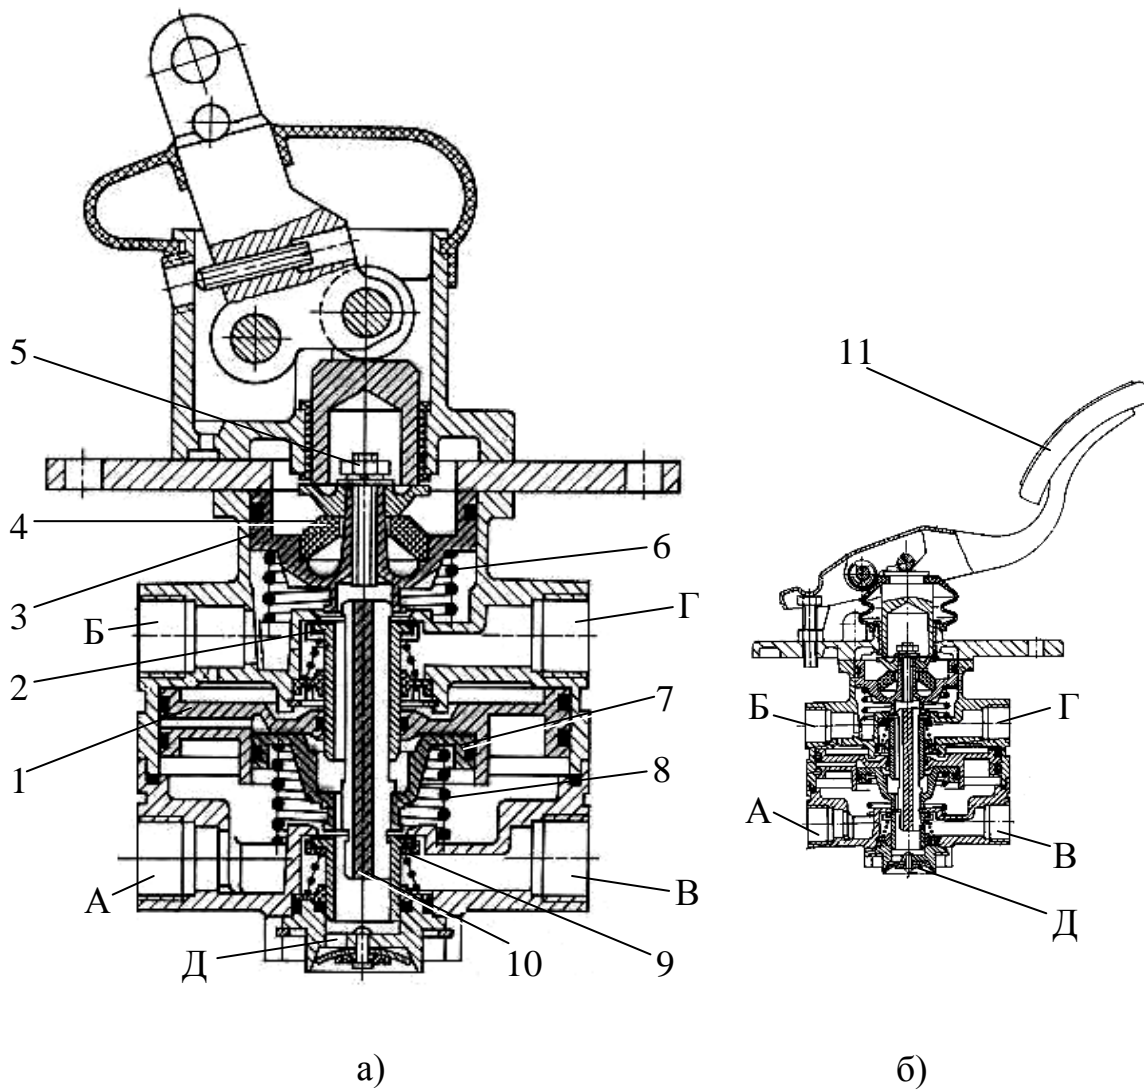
Двухсекционный тормозной кран грузового автомобиля-тягача КАМАЗ: а – с дистанционным приводом, б – с непосредственным приводом; 1 – ускорительный поршень; 2 – верхний клапан; 3 – верхний ступенчатый поршень; 4 – упругий элемент; 5 – упорный болт; 6 и 8 – пружины ступенчатых поршней; 7 – нижний ступенчатый поршень; 9 – нижний клапан; 10 – полый толкатель; 11 – тормозная педаль; А – вывод в контур № 1 привода тормозов рабочей тормозной системы передних колес и прицепа; Б – вывод в контур № 2 привода тормозов рабочей тормозной системы задней тележки и прицепа; В – вывод к ресиверу контура № 1; Г – вывод к ресиверу контура № 2; Д – вывод в атмосферу
